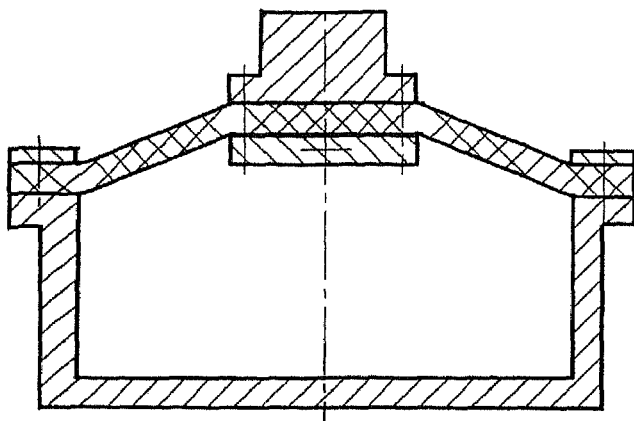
Пневматические амортизаторы для виброизоляции прессов
